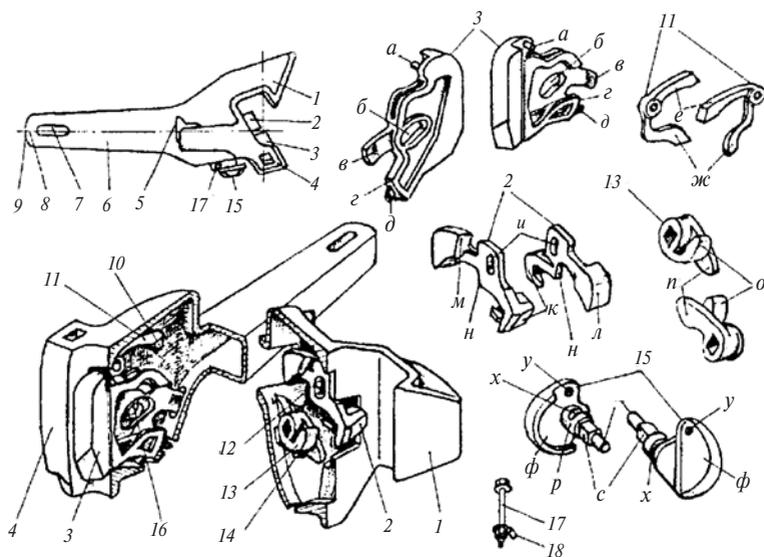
Устройство корпуса автосцепки и размещение деталей механизма сцепления внутри кармана:
